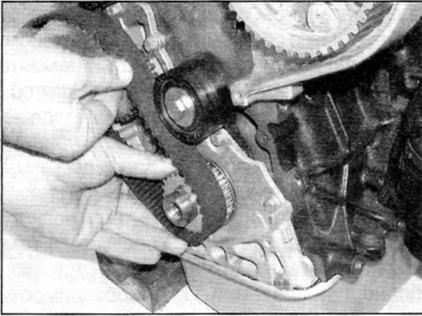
, а. Придержите ремень газораспределительного механизма на зубчатом шкиве коленчатого вала и пропустите его около промежуточного шкива...
